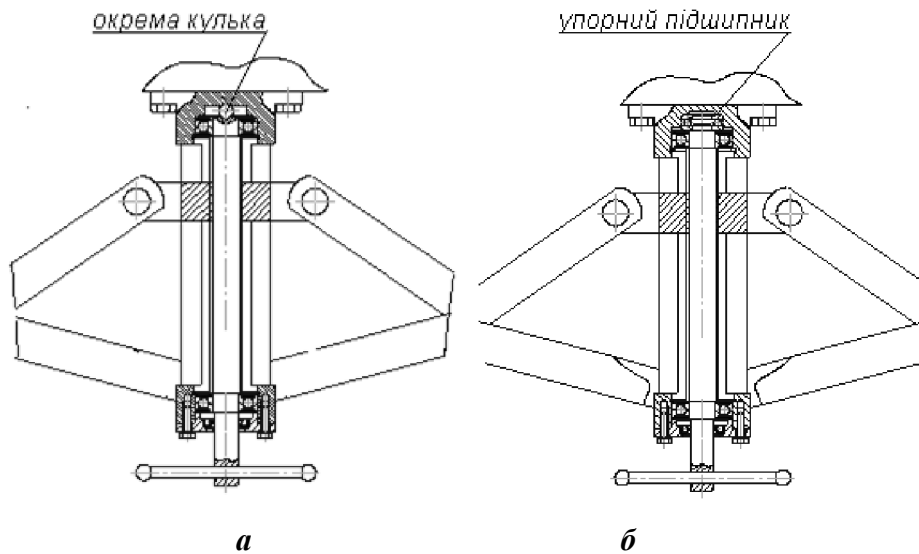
Загальний вигляд конструкції пероодачі гвинт-гайка: а – з окремою кулькою; б – з упорним підшипником
